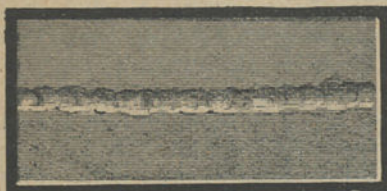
Soldadura autogenea de duas folhas de zinco.
